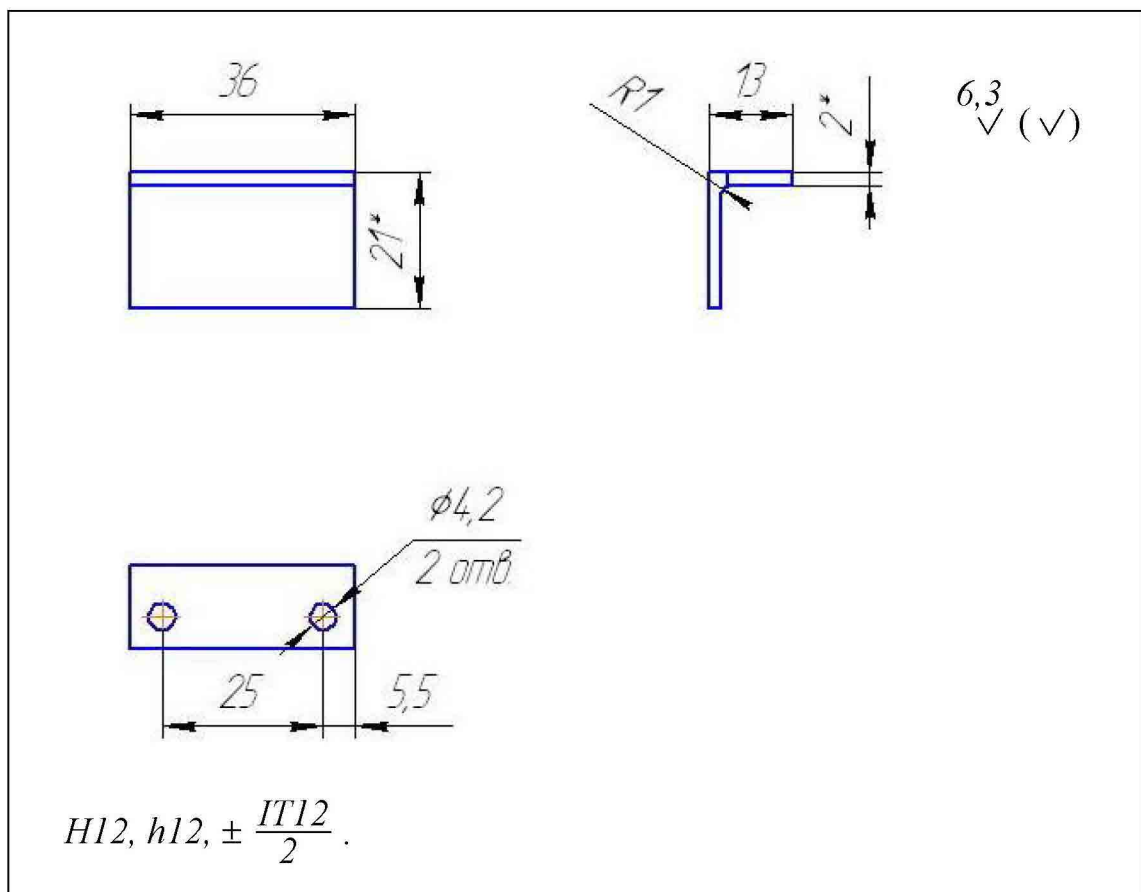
Кресленик деталі «Планка кріплення»
